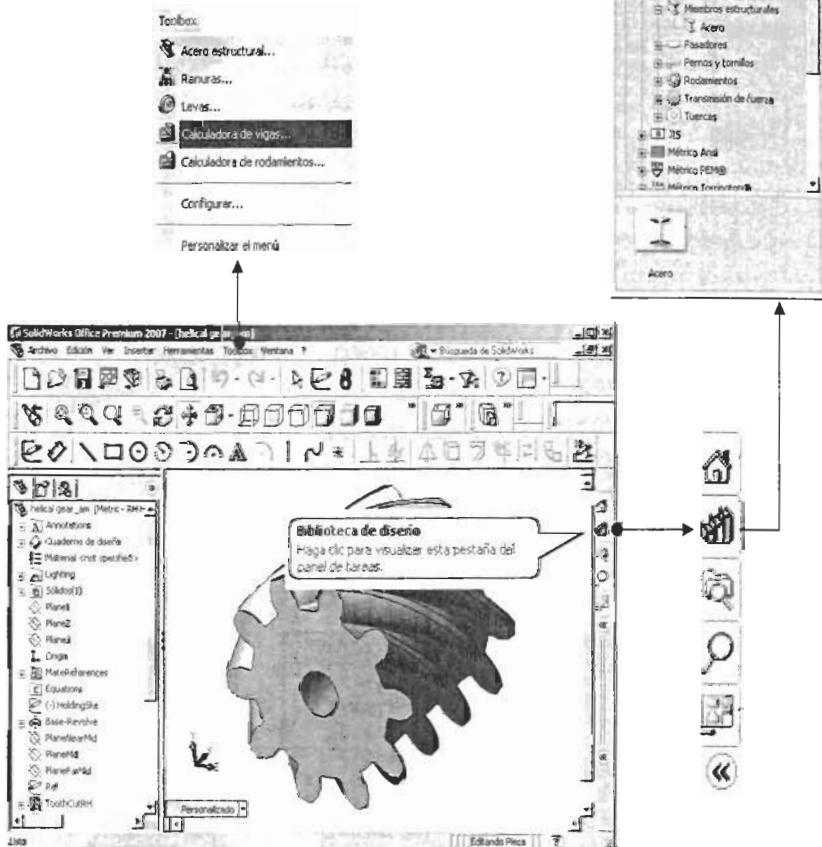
Engranaje helicoidal insertado desde Toolbox.
